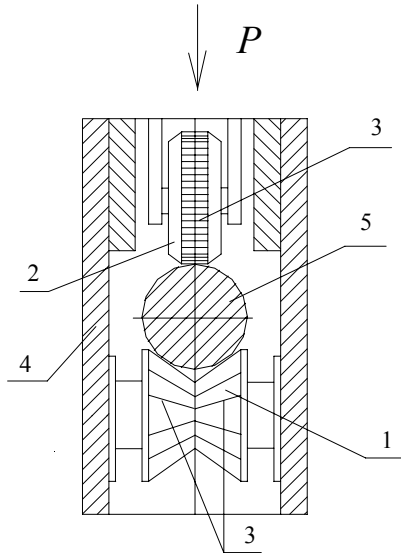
Схема зацепления заготовки валками тянущей клетки 1 – нижний валок, соединенный с валом электродвигателя; 2 – верхний прижимной валок; 3 – зубцы на поверхности валков; 4 – каркас тянущей клетки; 5 – заготовка
